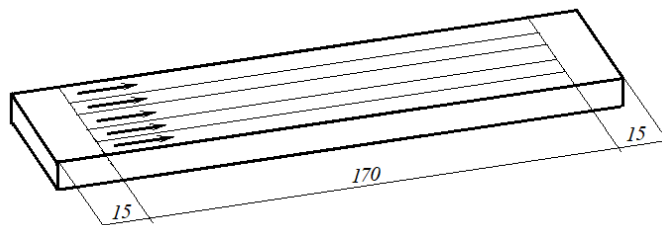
Схема движения лазерного пятна сканирования по поверхности образца
